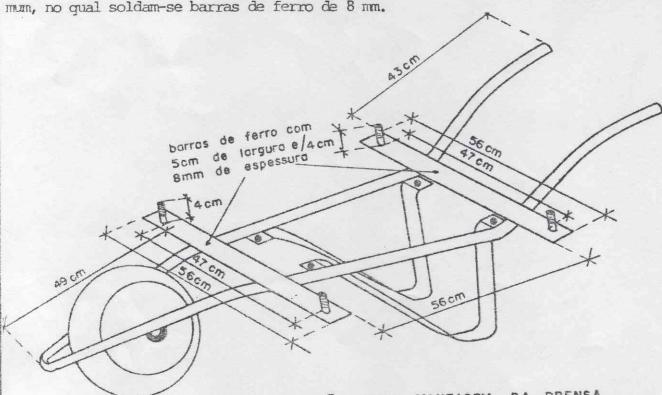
CHASSIS DO CARRO DE MÃO PARA MONTAGEM DA PRENSA
